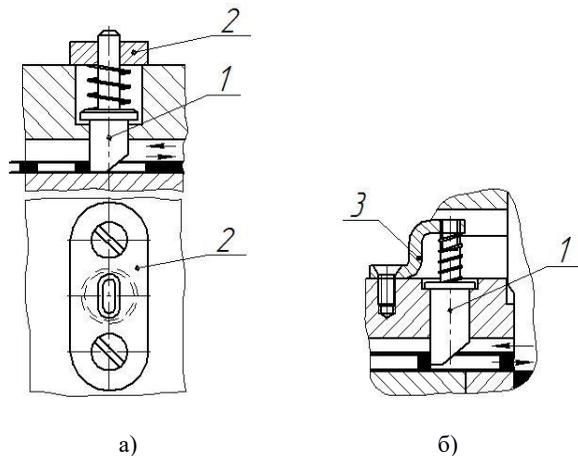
Подвижный упор двойного движения ленты (прямого и обратного):
